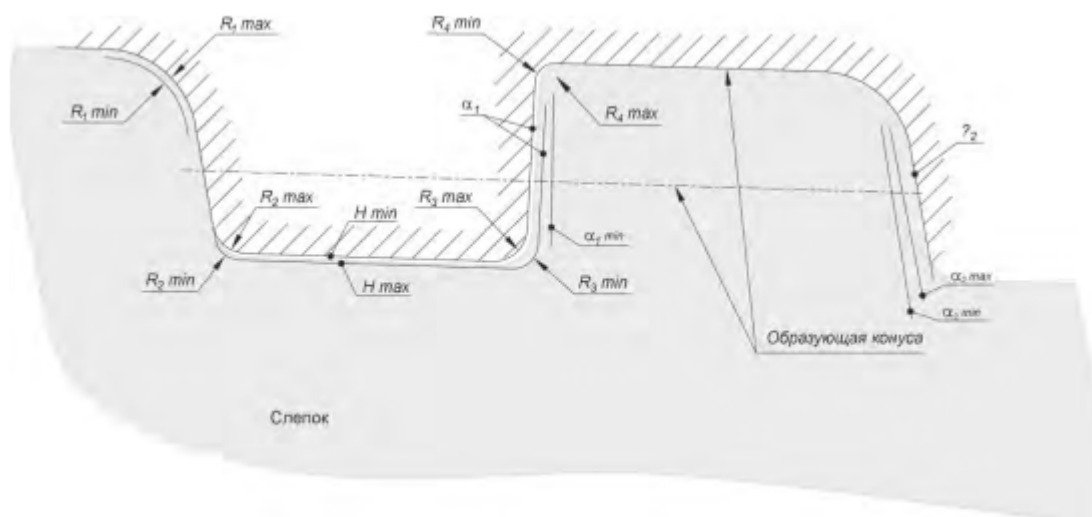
Контроль профиля резьбы муфты по слепкам
